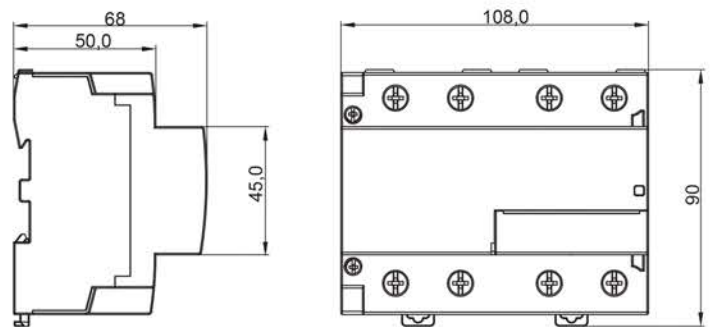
Габаритные размеры контакторов 100 А, 4P / Figure 6 – Overall dimensions of 100 A, 4P contactors
